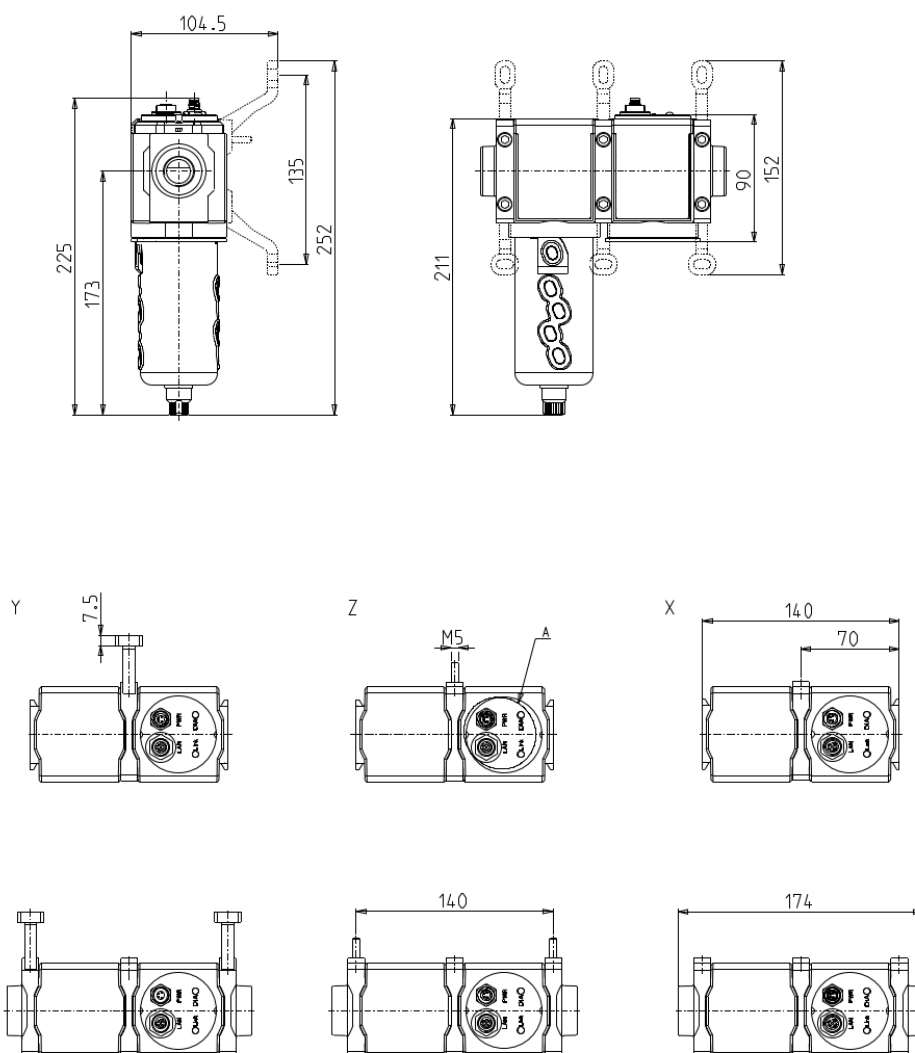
Dimensioni del sensore di flusso serie FSX3
